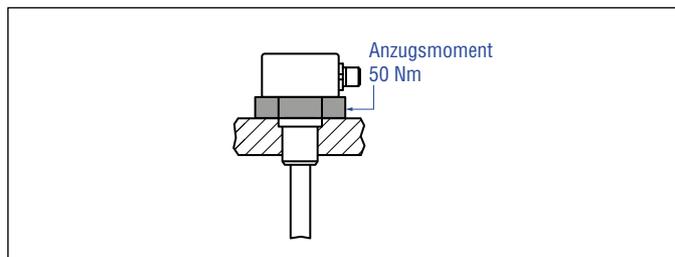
Einbaubeispiel für Gewindeflansch »M« & »T«
